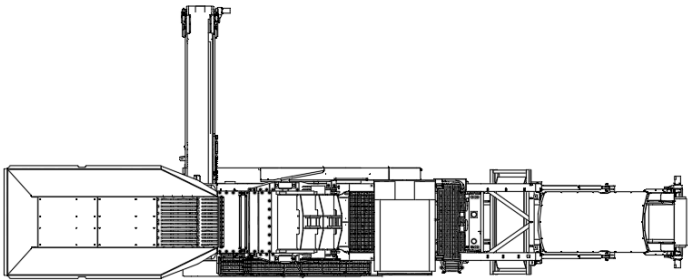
Esquema detalle de la planta de tratamiento de áridos fija.
